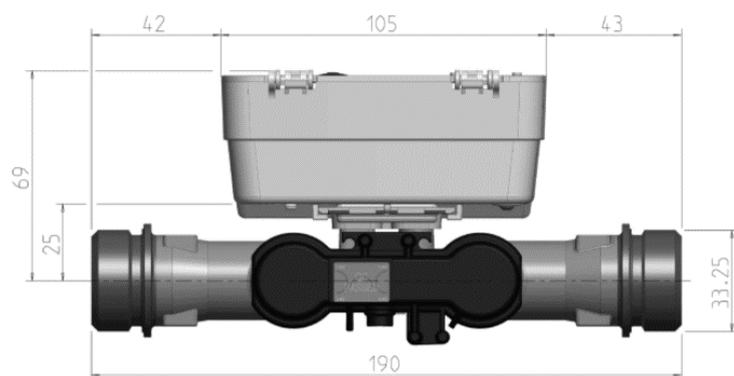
Übersicht Maße Baulänge 190 mm (Gewinde)
